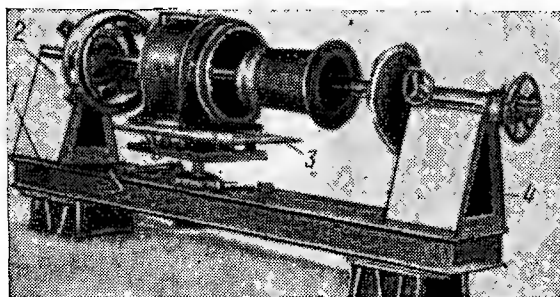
Станок для разборки и сборки вспомогательных машин:
